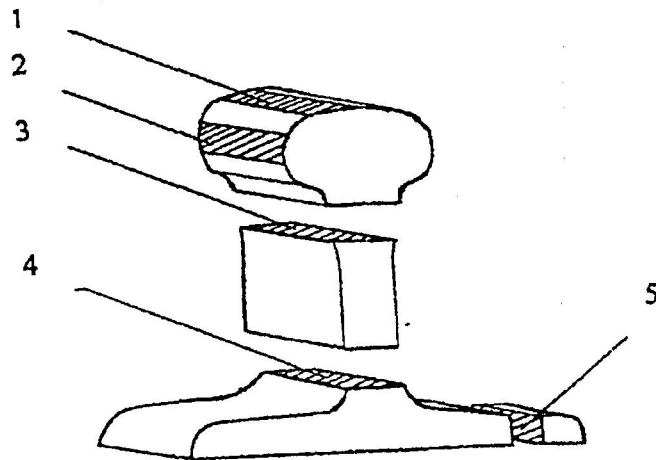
Зразки для дослідження мікроструктури зони термітного зварювання: 1 – поверхня кочення рейки; 2 – бокова поверхня головки рейки; 3 – шийка рейки, що розміщена біля головки; 4 – шийка рейки, що розміщена біля підшви; 5 – підшва рейки
